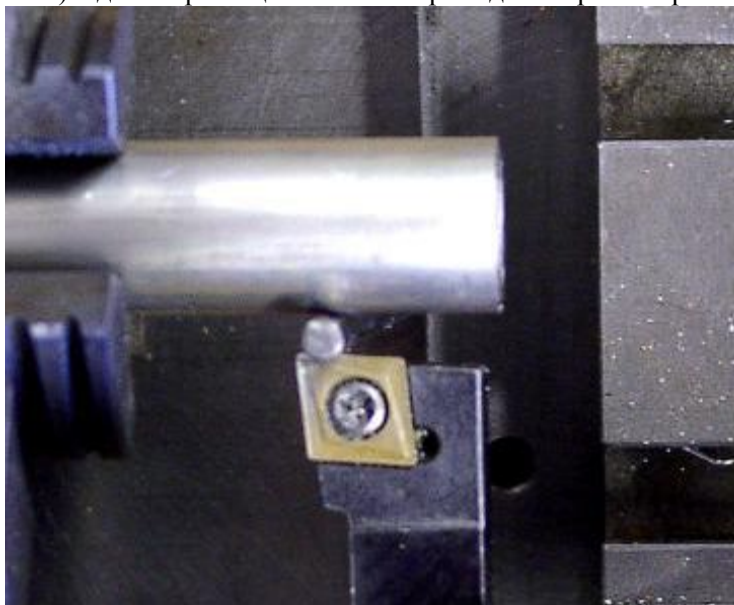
показывает положение, когда промежуток между резцом и заготовкой еще мал.
